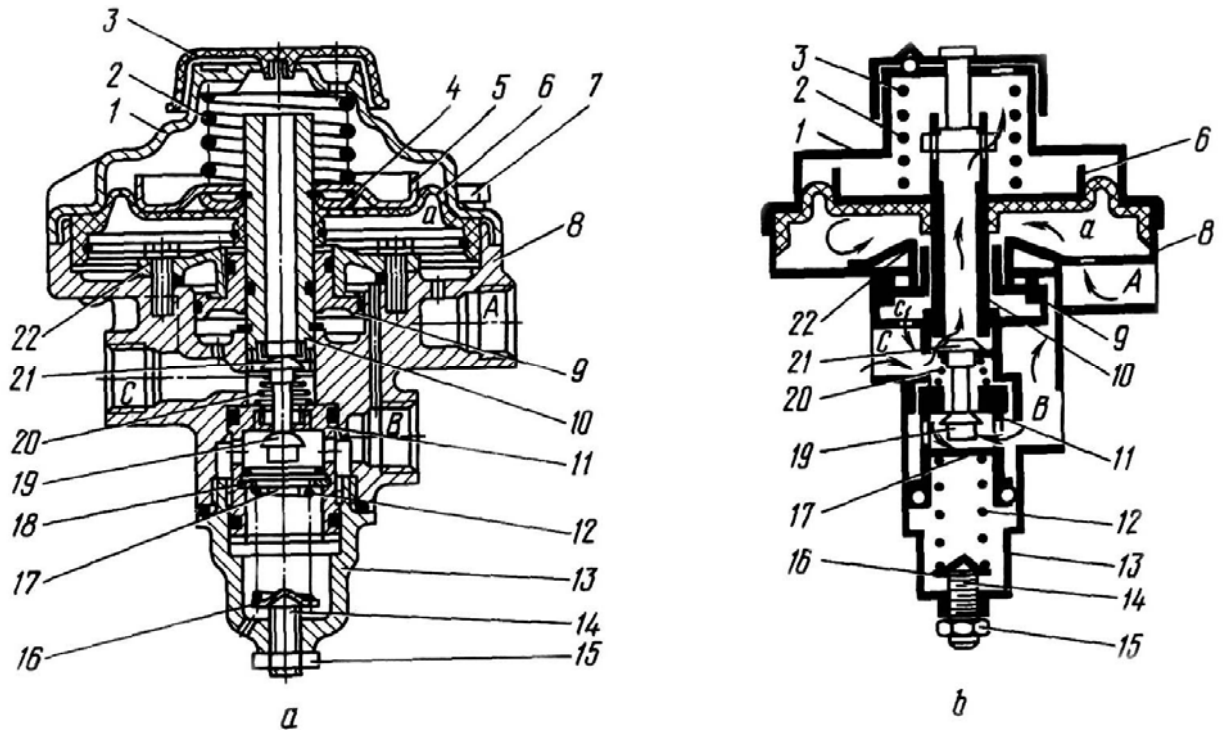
Клапан управления тормозами прицепа с однопроводным приводом: 1 - верхняя крышка; 2 - пружина; 3 - защитный колпак; 4 - малая шайба диафрагмы; 5 - большая шайба диафрагмы; 6 - диафрагма; 7 - болт; 8 - корпус клапана; 9 - поршень; 10 - толкатель клапана; 11 - поршень; 12 - пружина поршня; 13 - нижняя крышка; 14 - регулировочный винт; 15 - гайка; 16 - тарелка пружины; 17 - крышка клапана; 18 - упорное кольцо; 19 - впускной клапан; 20 - пружина клапана; 21 - выпускной клапан; 22 - опора верхнего поршня; а - исходное положение; б - положение при торможении
